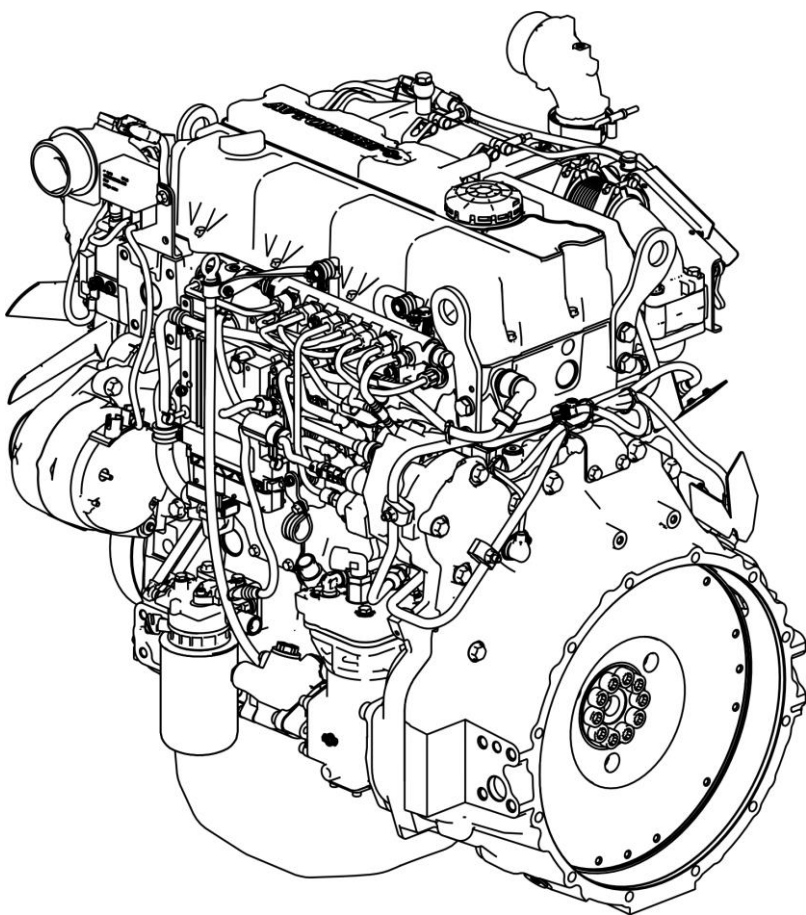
а – Двигатель ЯМЗ-53443-30 (общий вид слева)
